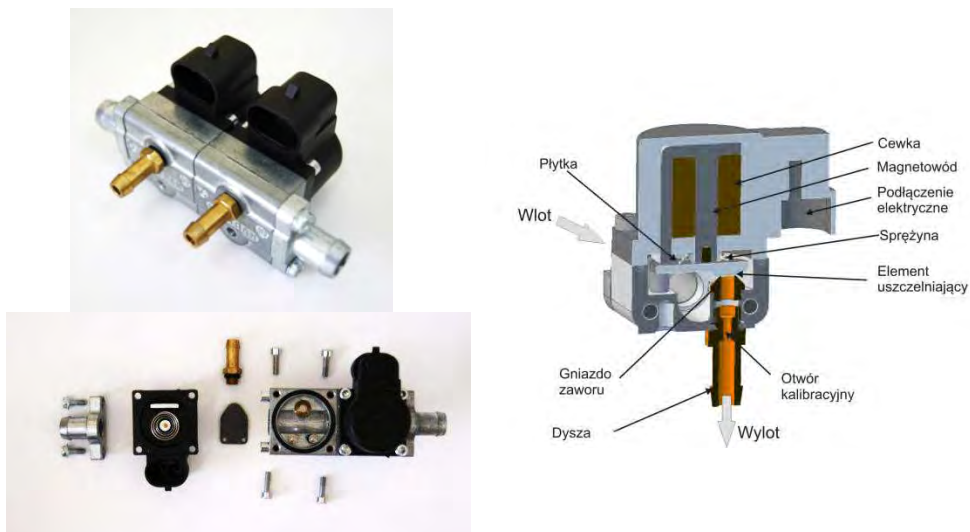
Konstrukcja wtryskiwacza Valtek typ 30
